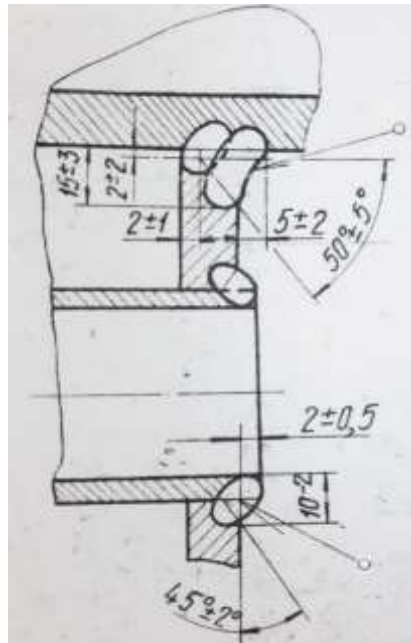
Сварное соединение трубы с трубной решеткой в котлах типа КАВ
